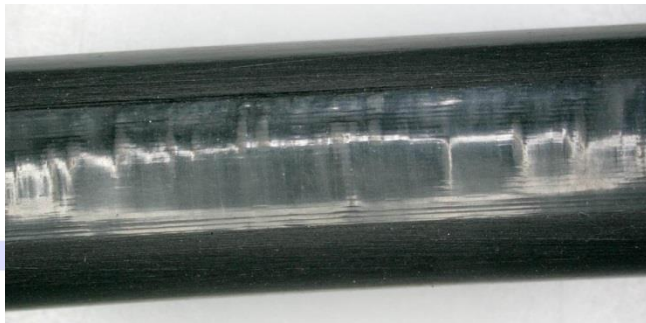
Unsymmetrisch abgeflachter O-Ring, die abgeriebene Oberfläche ist glatt und glänzend
